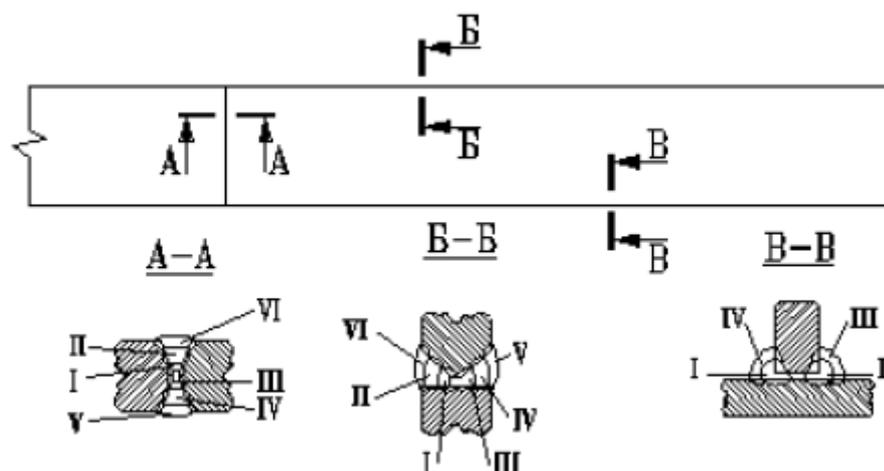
Последовательность сварки: а) по длине сварного шва;
